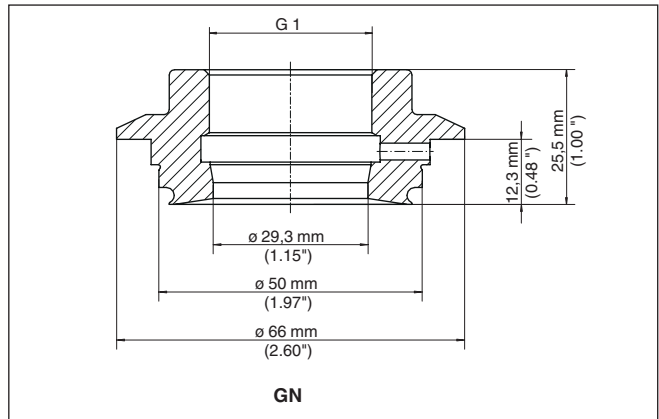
Maße Gewindeadapter G1 (DIN 3852-X) auf Varivent Form F 25
